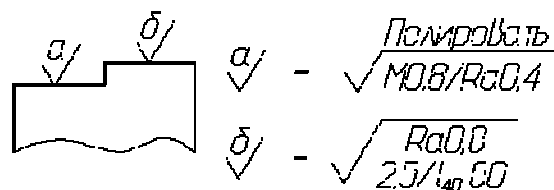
Пример упрощенного обозначения шероховатости поверхностей
